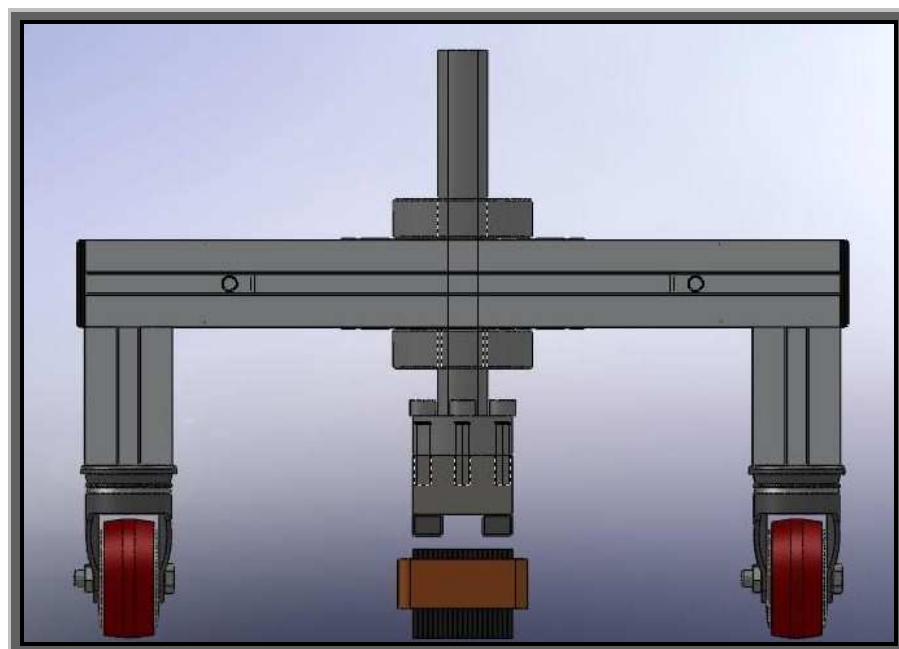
Vista isométrica del conjunto final del MLSIP.
